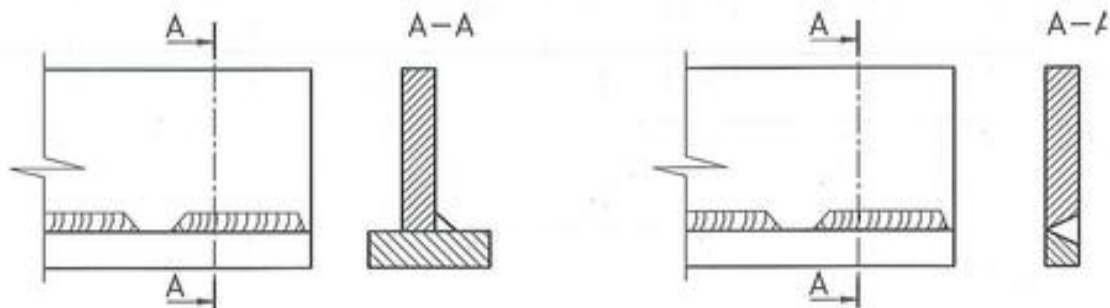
Corte de un cordón de soldadura discontinuo.
